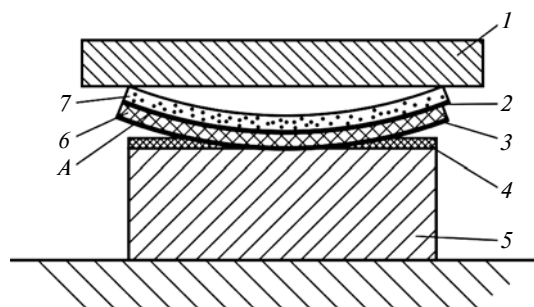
Способ изготовления колодки упорного подшипника скольжения из листа фольгированного фторопласта:
